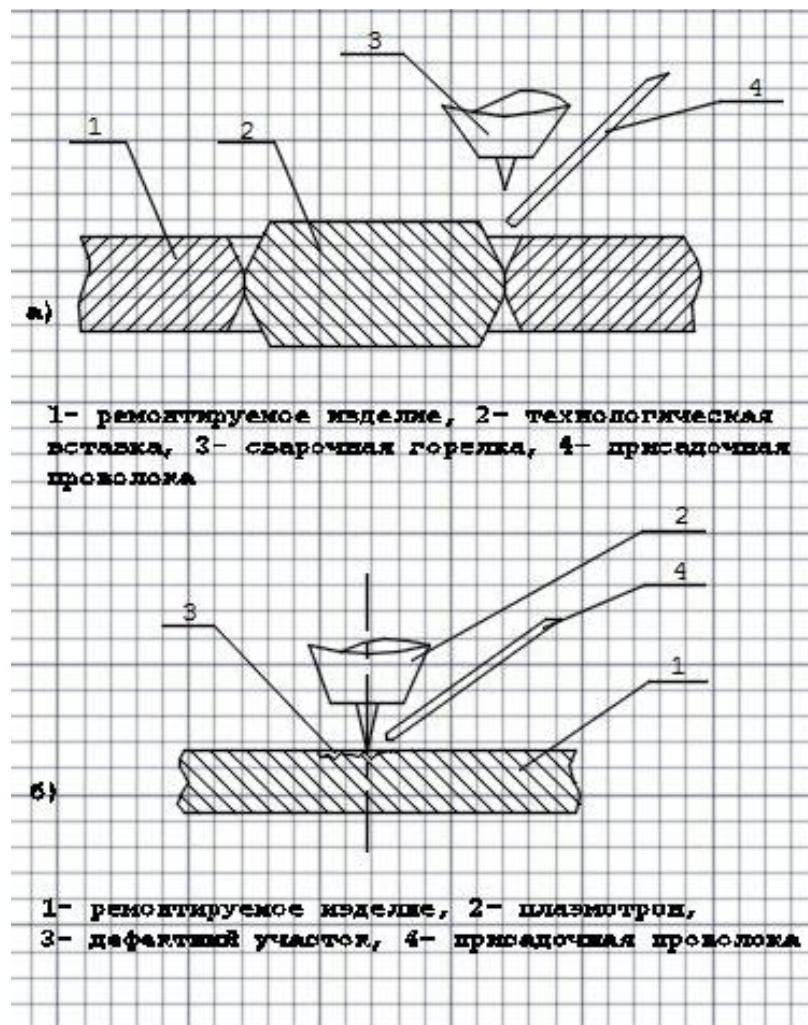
Ремонт микроплазменной сваркой
